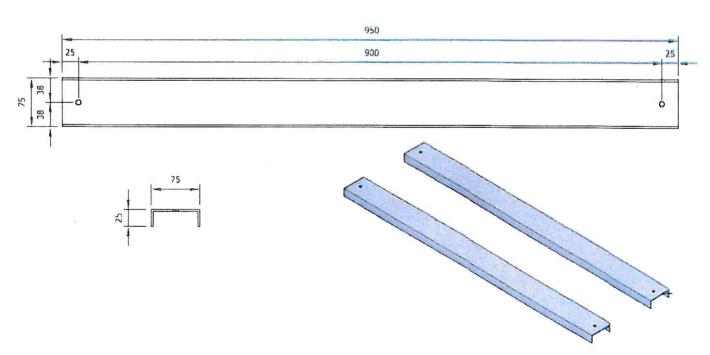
Rails de fixation sur tôles ondulées (partie haute).
